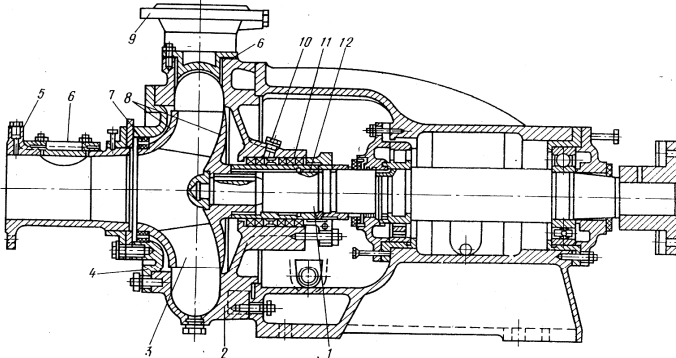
Насос типу СД: 1- вал; 2- корпус; 3- вхідний патрубок; 4- передня кришка корпусу; 5- вхідний патрубок; 6- люки ревізії; 7- захисні ущільнюючі кільця; 8- передні і задні диски робочого колеса; 9- вихідний патрубок; 11- сальникове ущільнення; 12- захисна втулка
